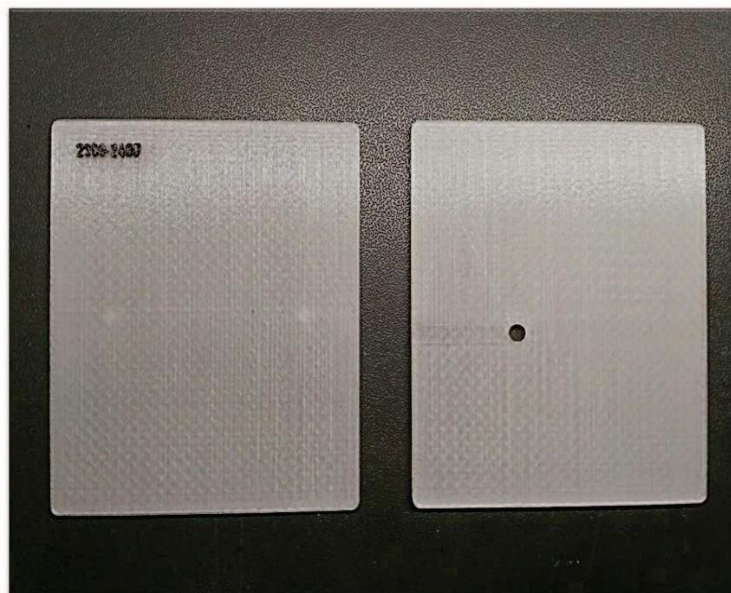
Зовнішній вигляд роздрукованого корпуси
